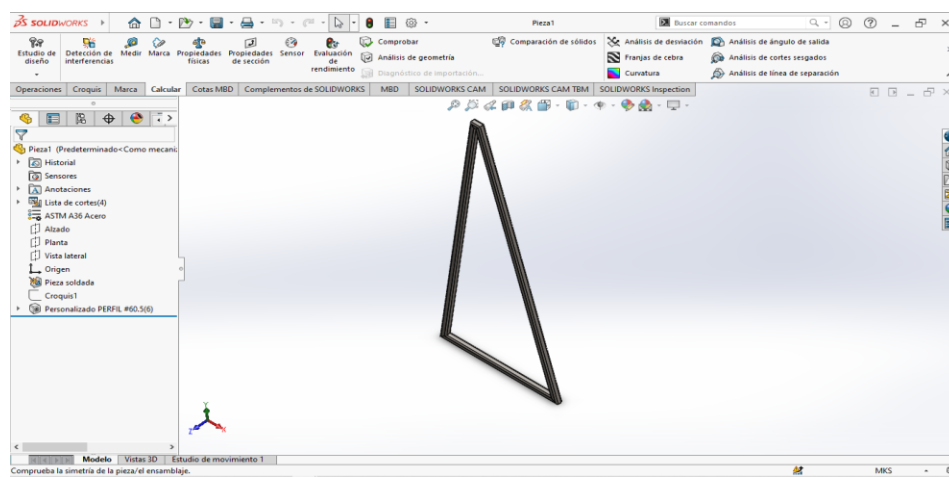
Diseño de la estructura - perfil #60.5, material acero A-36. Fuente: Autor
